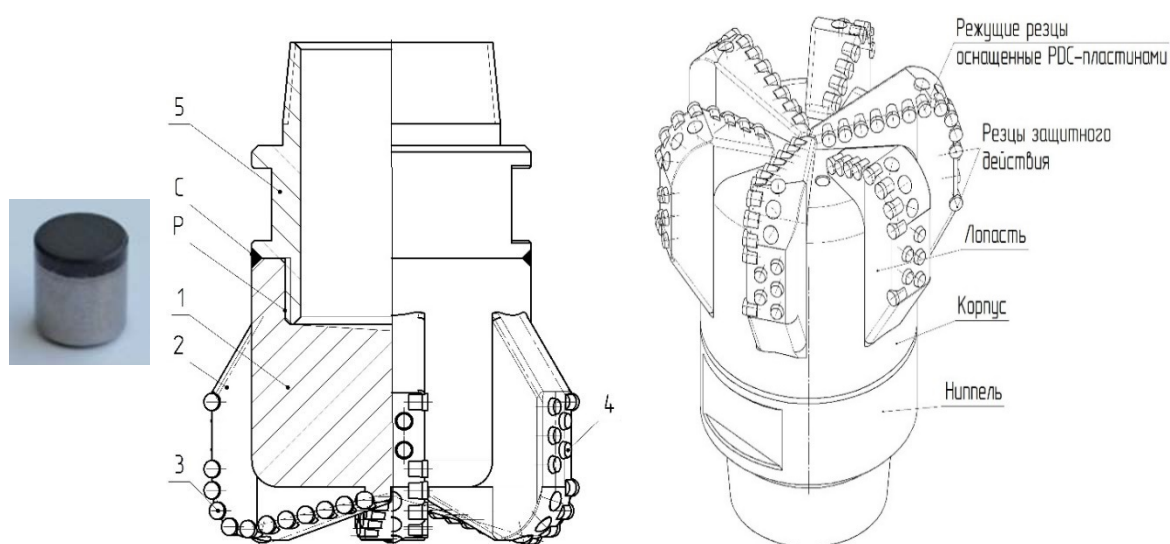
Алмазное долото: 1 – корпус долота; 2 – лопасти; 3 – режущие зубки с алмазонасным слоем; 4 – резцы защитного действия; 5 – ниппель; P – резьбовое соединение; C – сварочный шов
